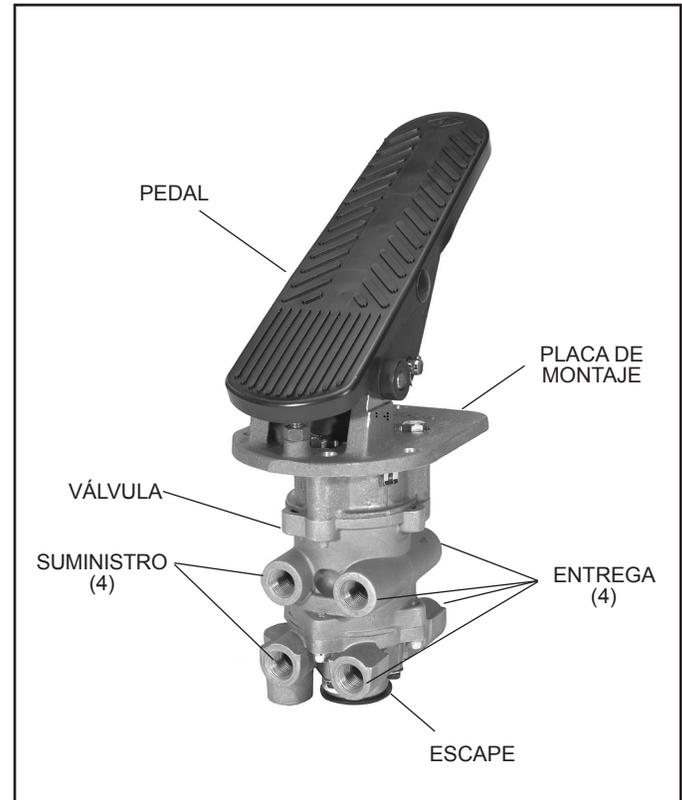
VÁLVULA DE FRENO DOBLE E-10P™ DE BENDIX®
